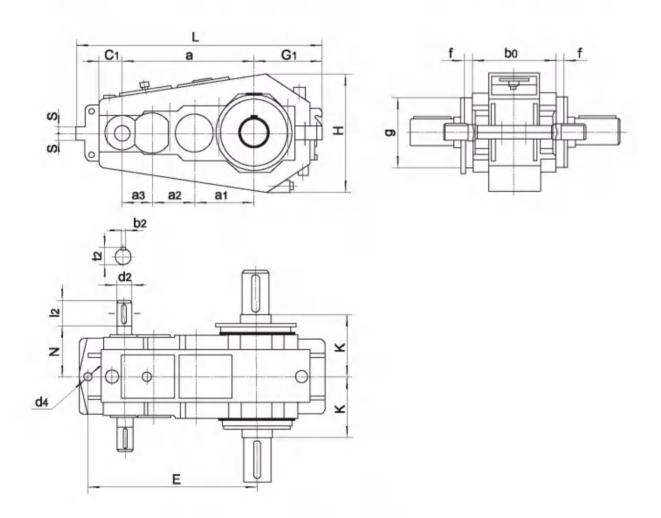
QY3S减速器外形尺寸 Figure 6 External dimension of QY3S decelerator
